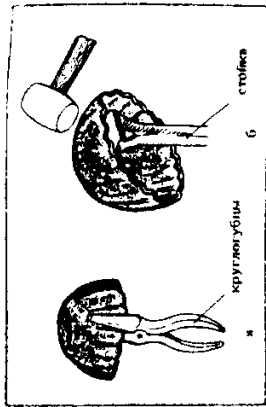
Обформление сферы: а — изготовление гофры; б — осадка гофры
